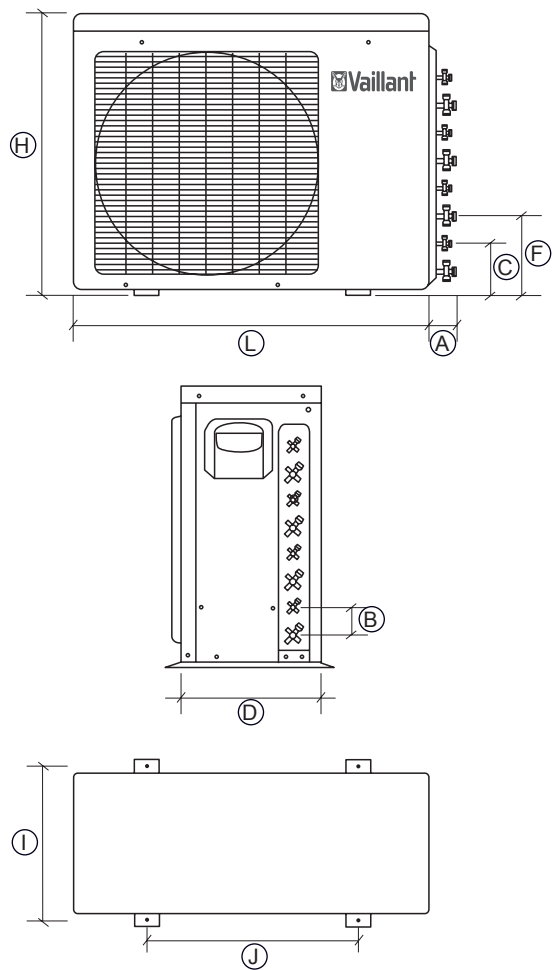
Dimensiones de la unidad exterior VAF 6-085 W4NO.
